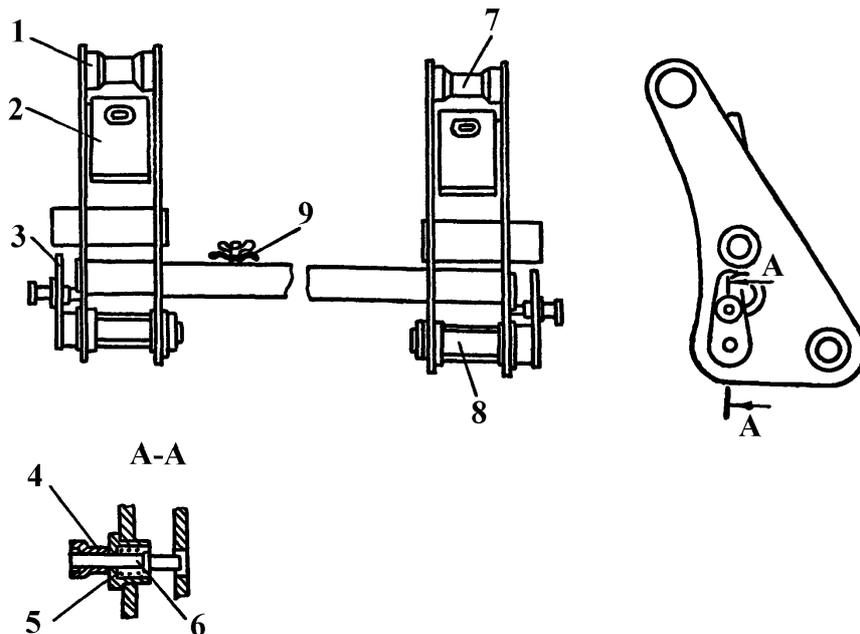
Устройство сменных рабочих органов машин МТП-441 и 441-01: 1 – переходник; 2 – упор; 3, 4 – ручки; 5 – пружина; 6 – ось; 7 – палец верхний; 8 – палец нижний; 9 – планка прижимная
